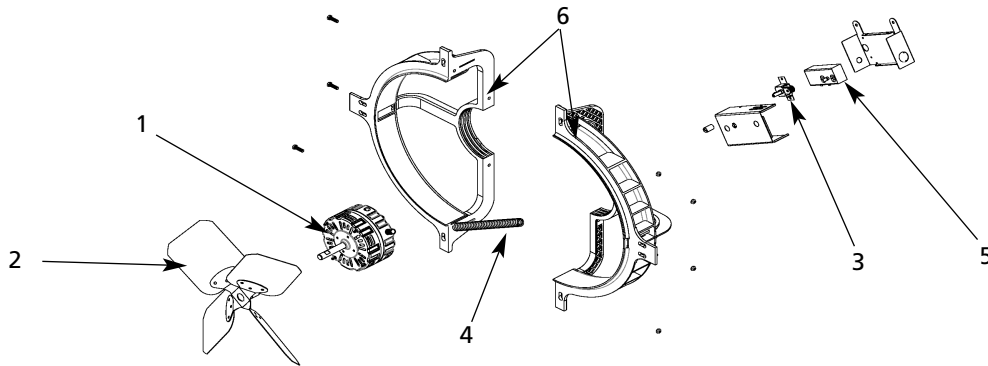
Ilustración de las Partes de Ventiladores de Montaje de Frontón Automático de Carcasa Metálica
